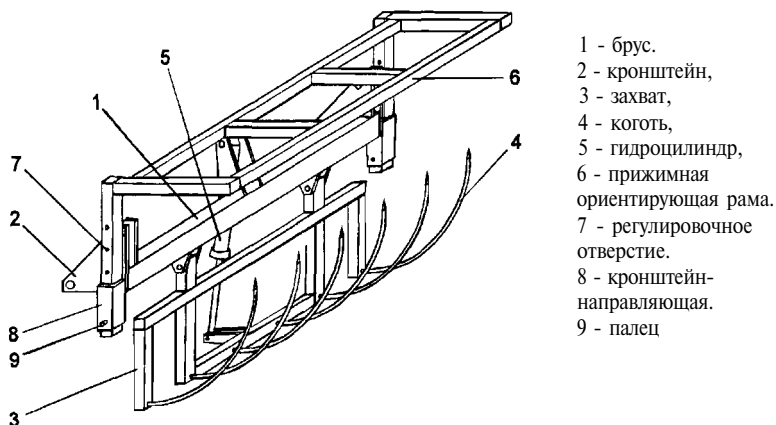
Схема вилочно-когтевого грузозахватного устройства
